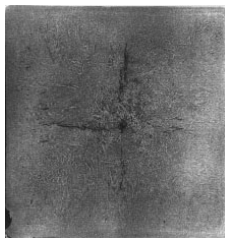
Осьова тріщина в безперервнолитої заготовці
